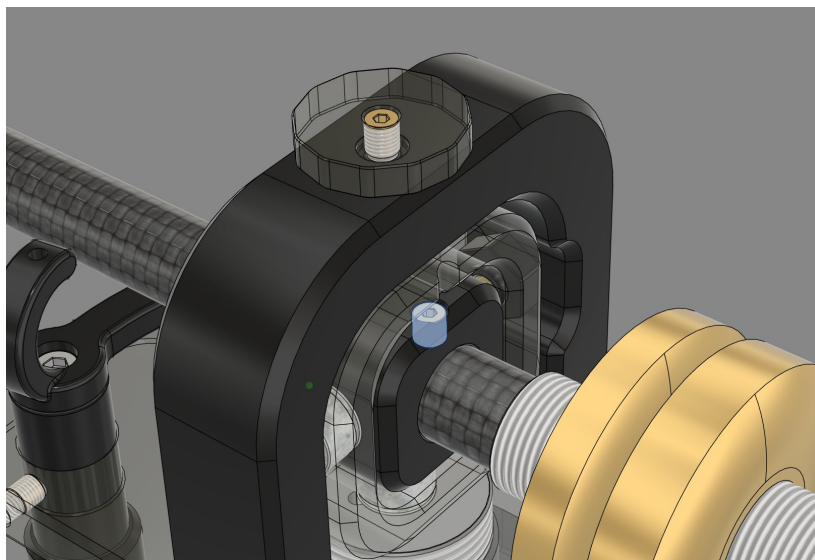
Diese Schraube fixiert das Armrohr am inneren Lagerblock
